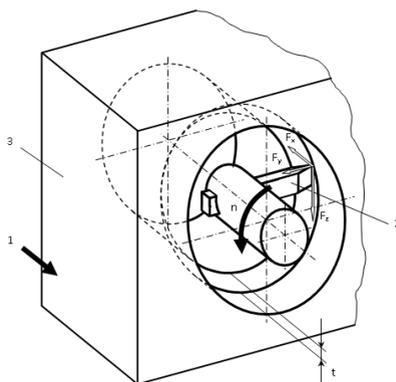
Эскиз растачивания: 1 – направление движения подачи;
